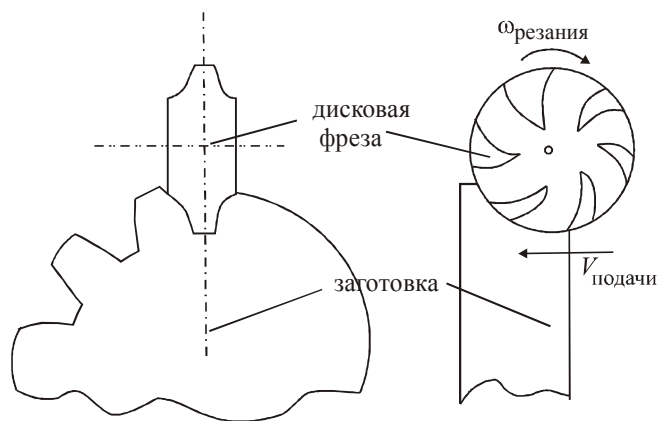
Нарезание зубчатого колеса методом копирования дисковой фрезой
